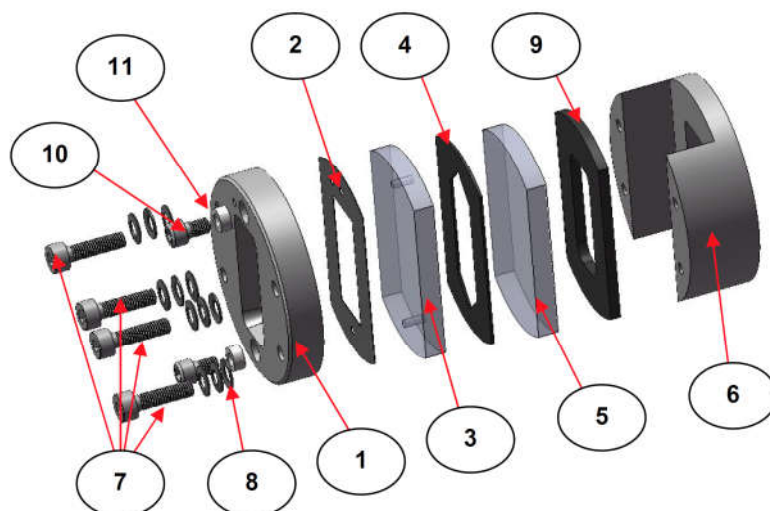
Explosionszeichnung der verwendeten Dünnschichtküvette (Specac) [80].
